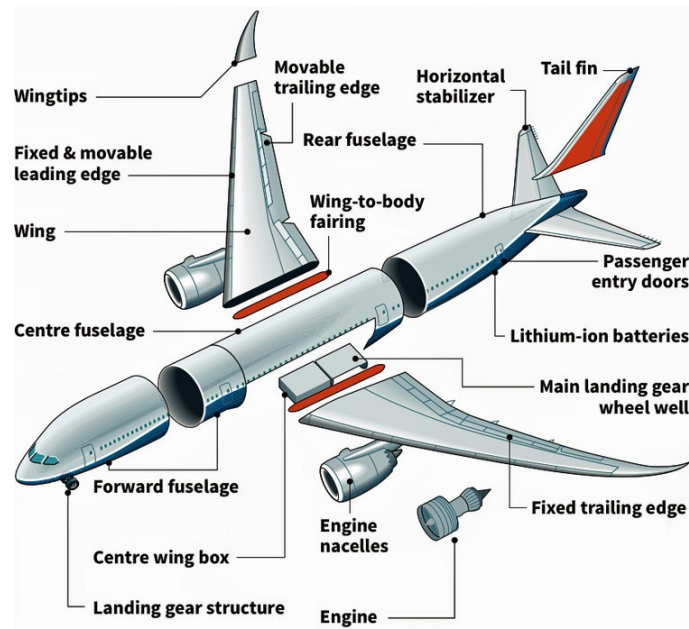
Parts principals del fuselatge d'un Boeing 787 Dreamliner (Reuters)
